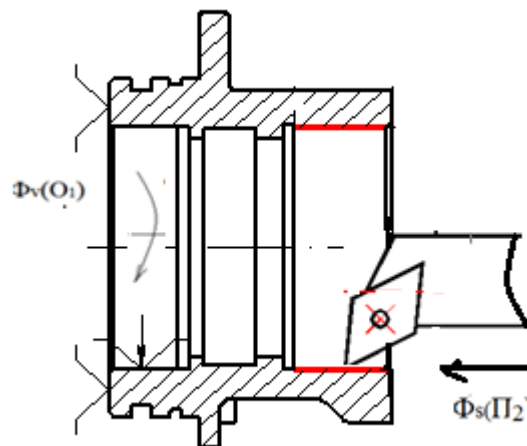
Рухи при обробленні внутрішньої поверхні
